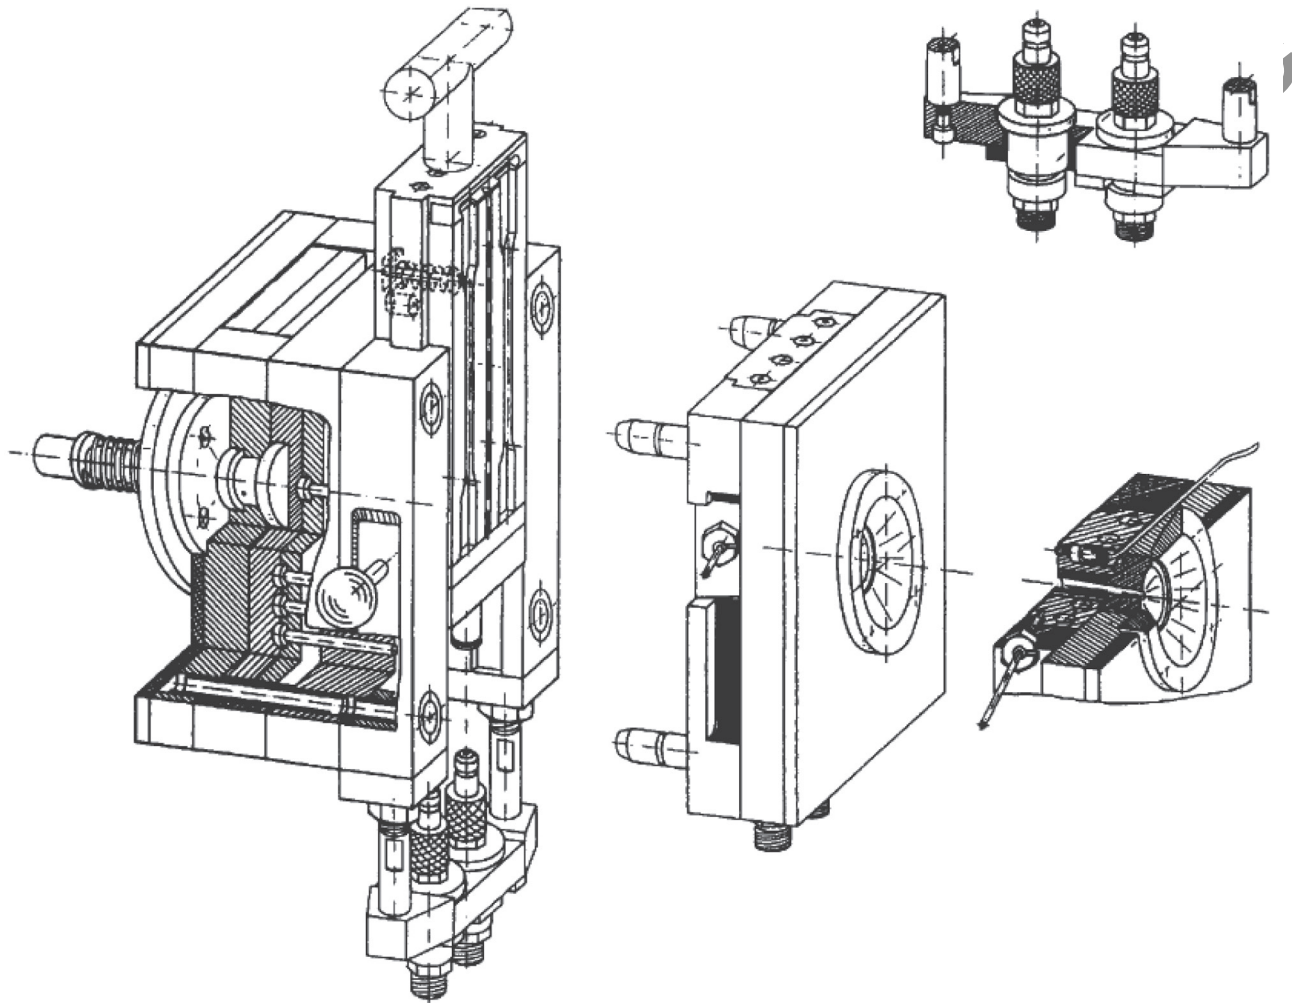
Vue éclatée d'un moule pour moulage par injection à plaque de deux cavités interchangeables pour un moule ISO 20753 de type A1
